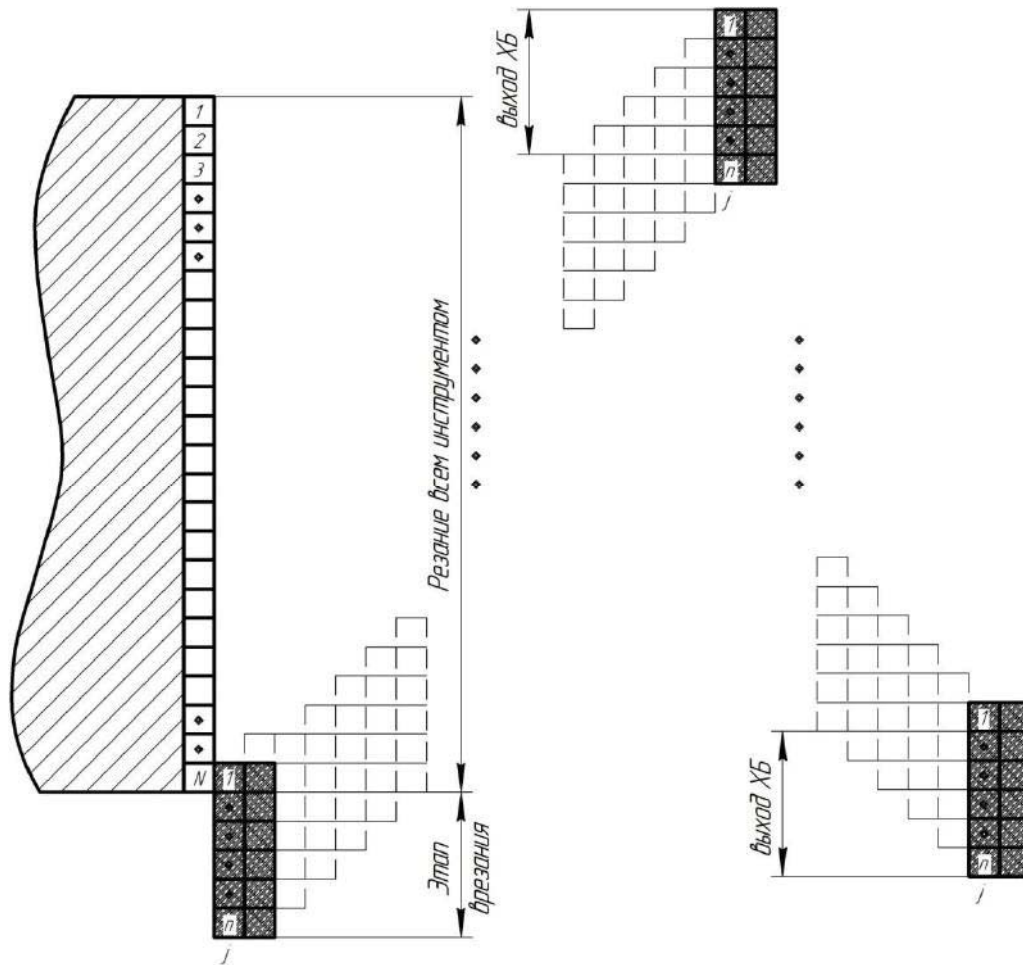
Схема перемещений хонинговального бруска относительно поверхности заготовки
